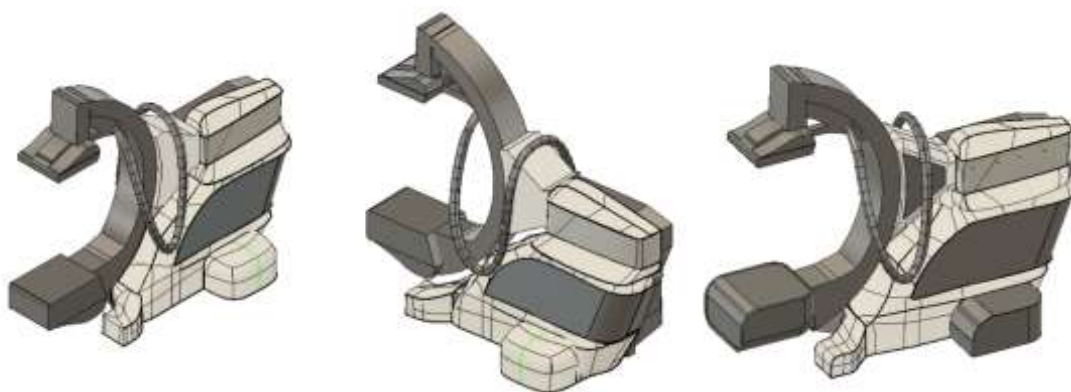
Вариант с металлической гнутой боковой крышкой
